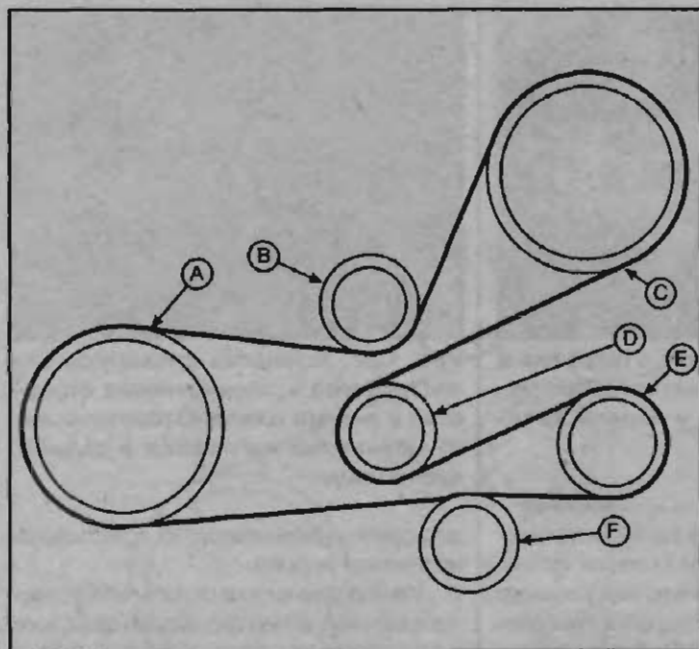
Расположение ремня привода навесных агрегатов на шкивах дизельного двигателя без системы кондиционирования воздуха: А – шкив коленчатого вала; В – шкив автоматического механизма натяжения ремня; С – шкив насоса усилителя рулевого управления; D – эксцентриковый шкив механизма натяжения; Е – шкив генератора; F – направляющий шкив
